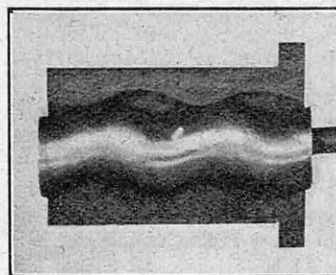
COUPE DU STATOR DANS LEQUEL SE TROUVE LE ROTOR VU NON COUPÉ
